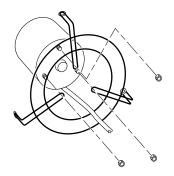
Retrait ou fixation de la grille de ventilateur sur le moteur
